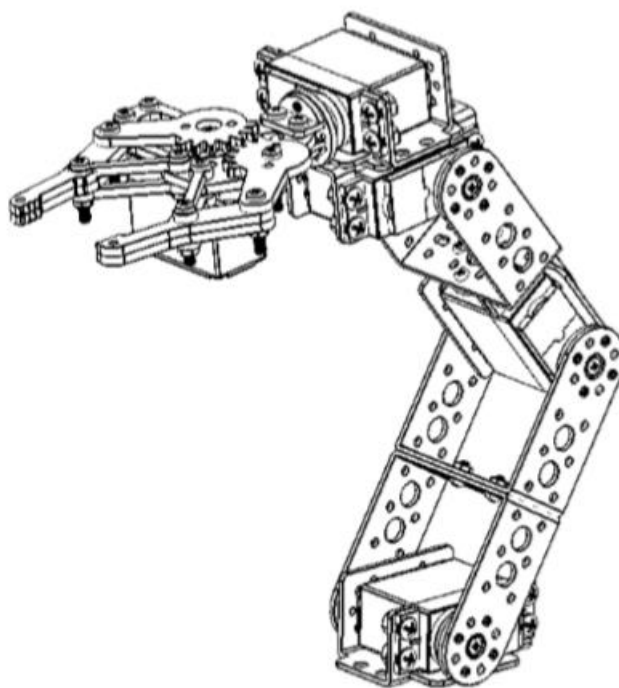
Внешний вид части руки манипулятора
